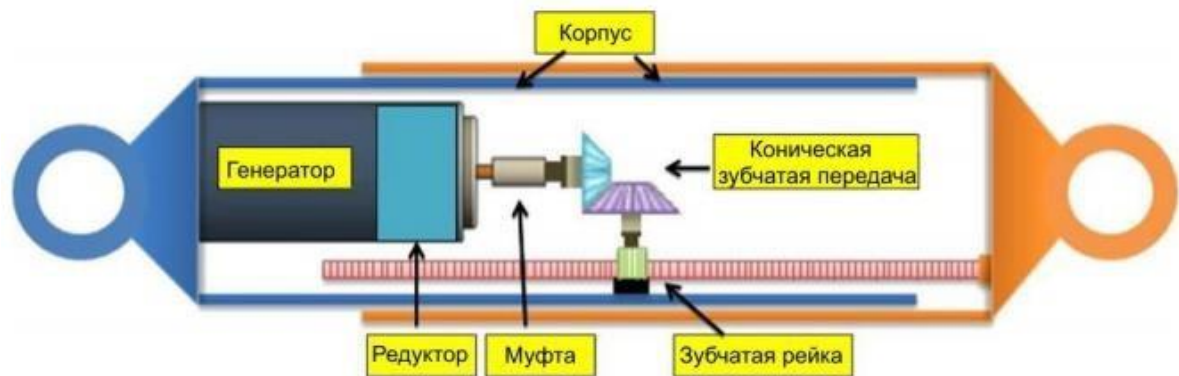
Конструкція регенеративного амортизатора з механізмом приводу, що складається з рейкової та конічної передачі
